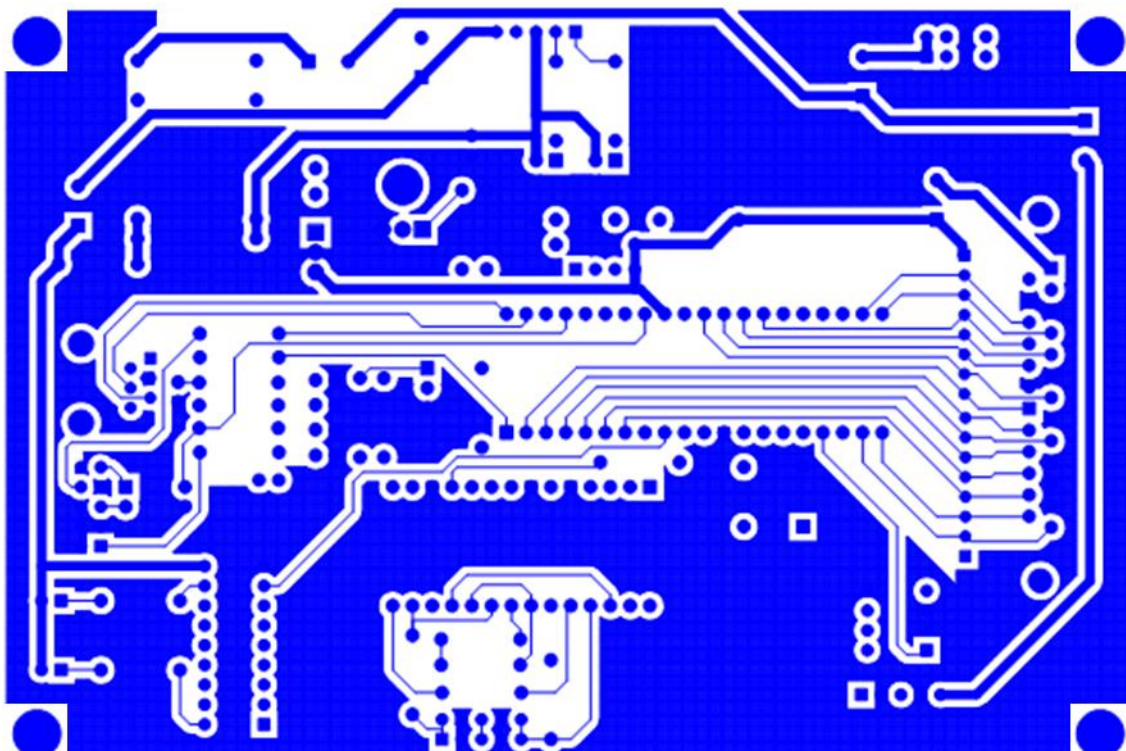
Placa del módulo de control Layout final. Capa BOTTOM
